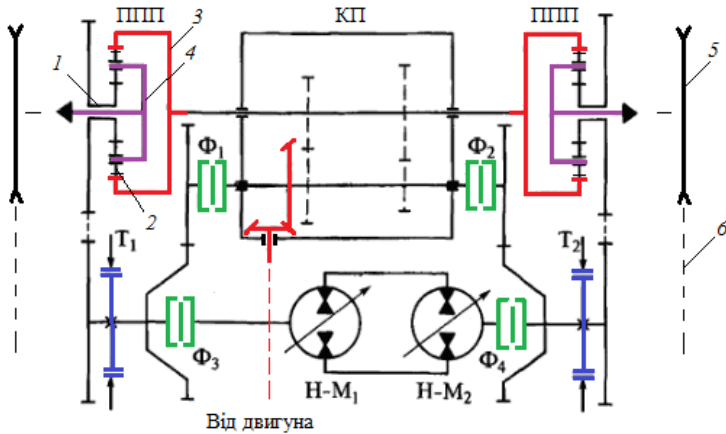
Схема безступінчастих механізмів повороту другого типу гусеничних машин: КП – коробка передач; ППП – підсумовуюча планетарна передача; Φ_1 - Φ_4 – фрикціони; T_1 - T_2 – стрічкові гальма; М – гідромотор; Н – гідронасос; 1 – сонячна шестерня; 2 – сателіт; 3 – епіциклічна шестерня; 4 – водило; 5 – ведуче колесо; 6 – гусенична гілка
